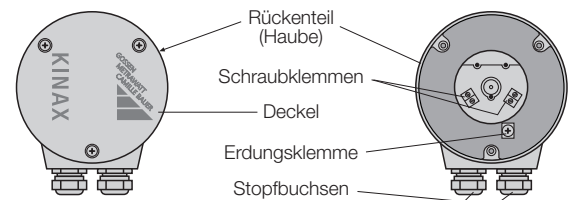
KINAX WT 707 mit Schraubklemmen und Stopfbuchsen.
